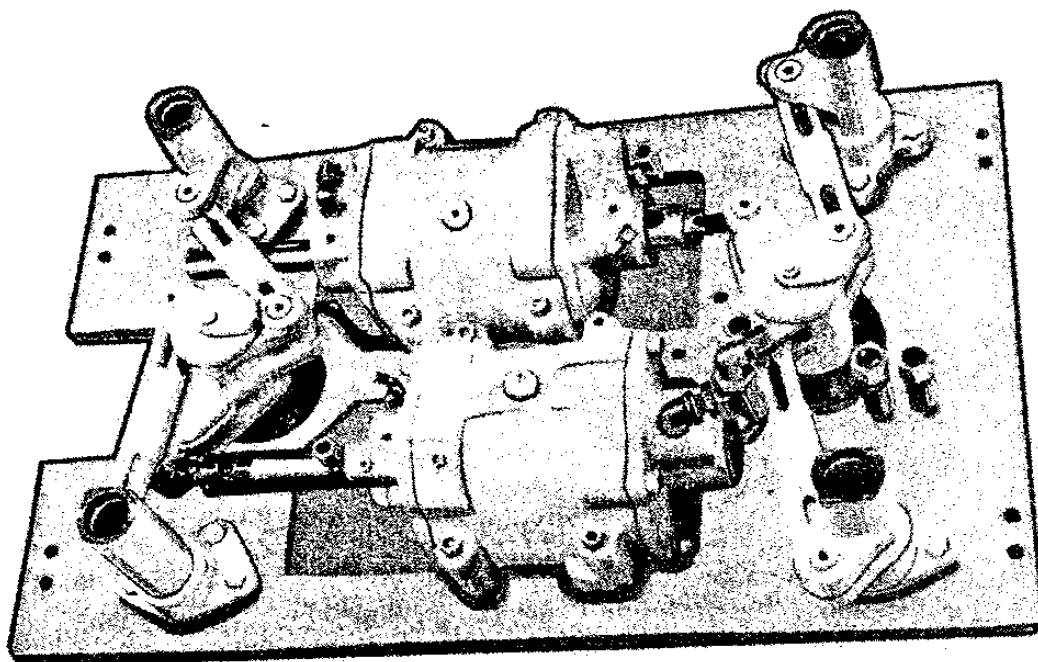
Mecanismo de Abrir y Cerrar Molde.
